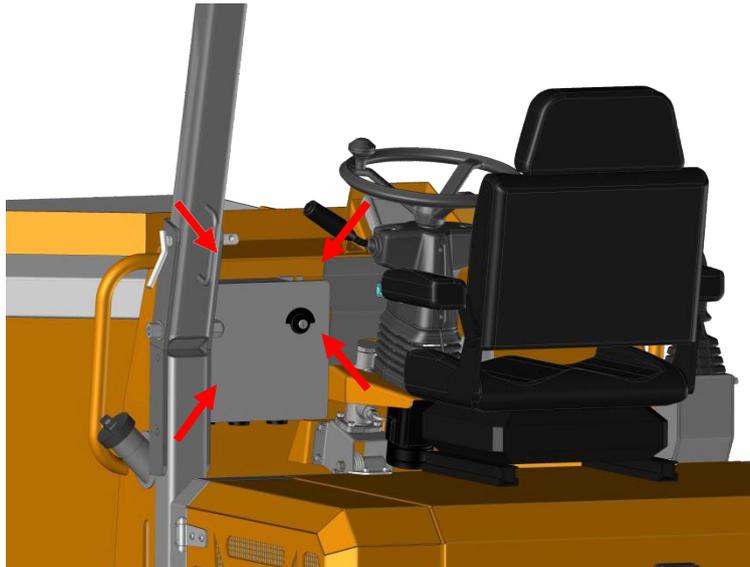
Plattform für den Zugang zum Ölfilter
